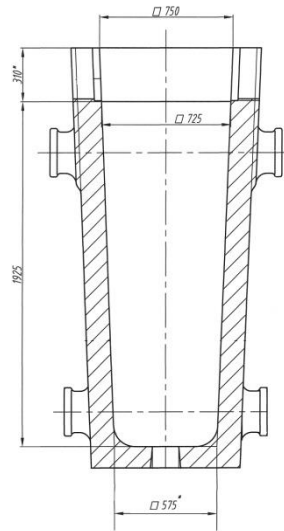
Эскиз изложницы для отливки слитков с уменьшенной прибыльной частью
